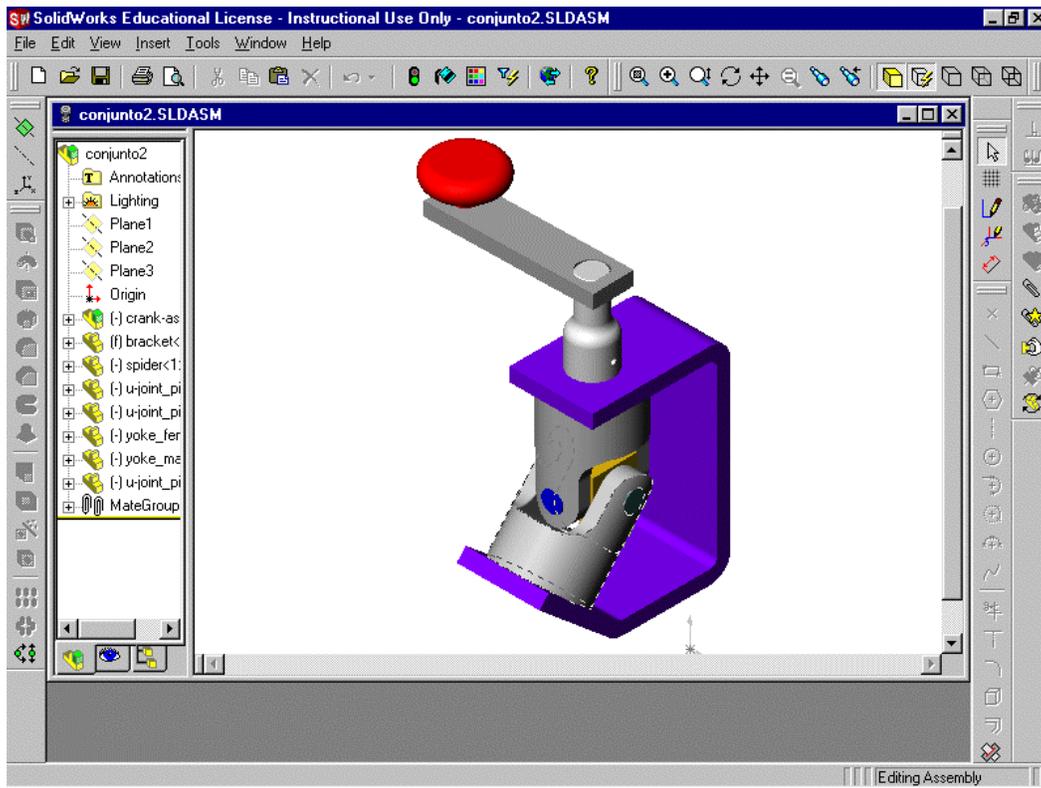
Interface Assembly (montagem). Representação de um dispositivo em perspectiva
